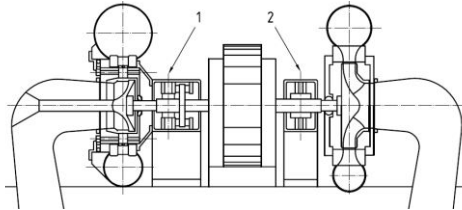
Máquina horizontal con cojinete de pedestal [18]
